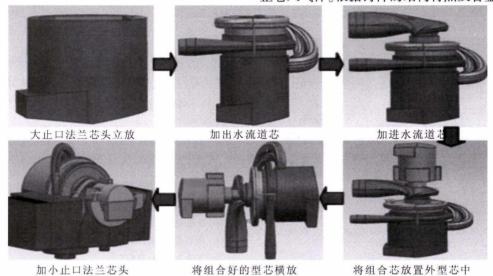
型芯组装示意图 Fig.6 Core assembly diagram
